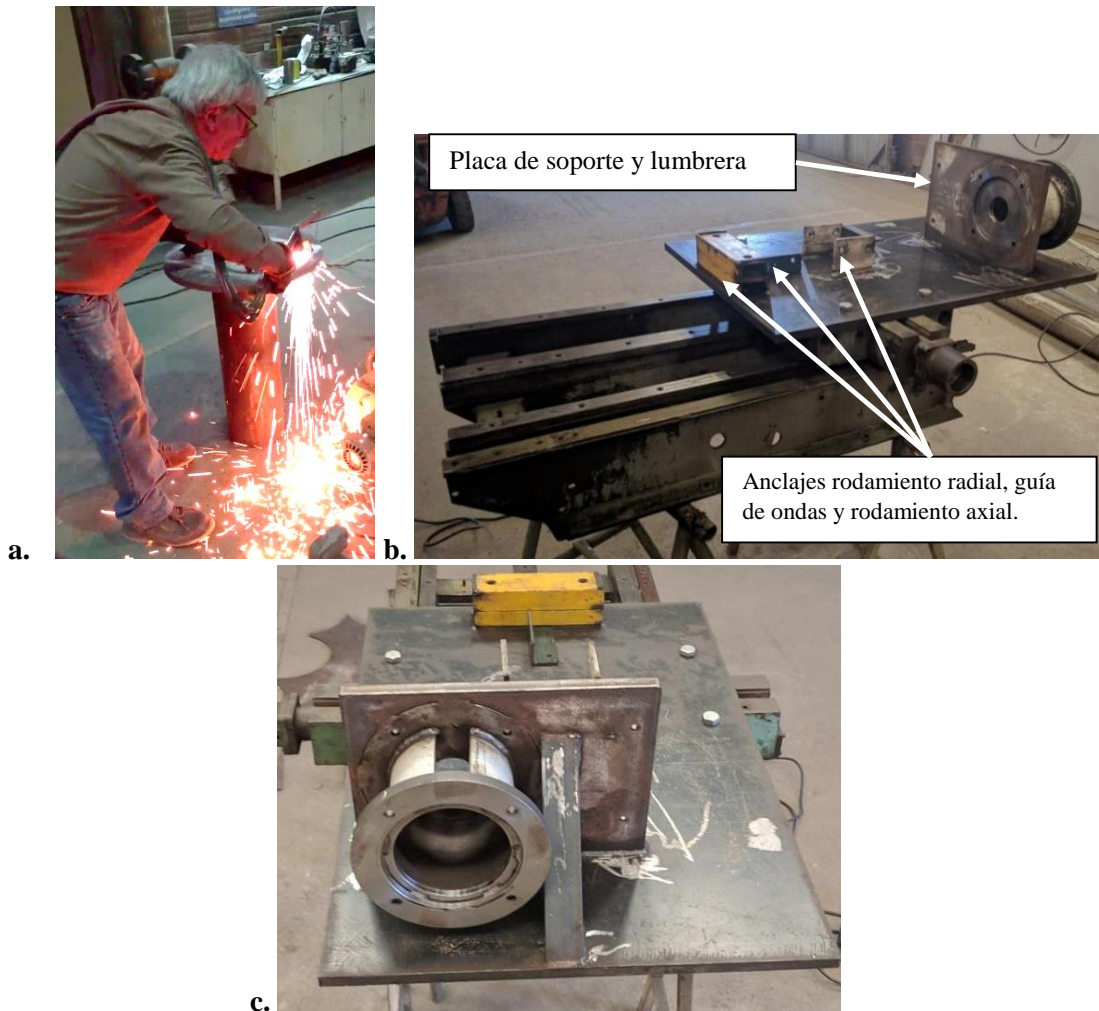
a. Corte manual de la placa de anclaje. b. Posición soldada de los anclajes sobre la chapa base. c. Vista principal de la lumbrera de conexión y el soporte motor - caja reductora.
